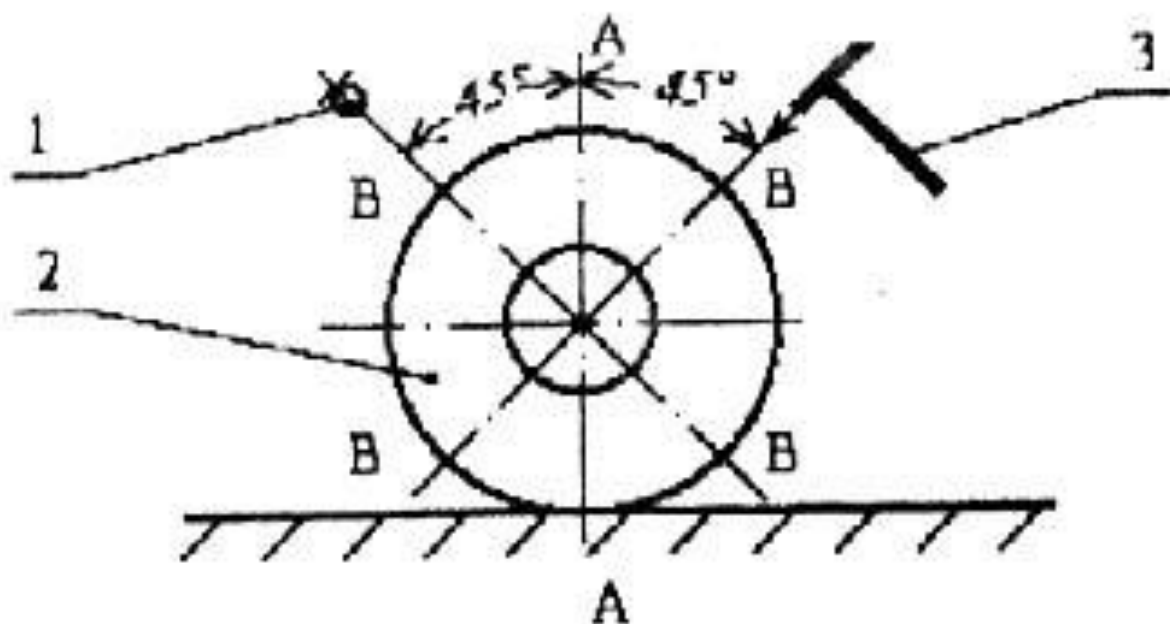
Схема расположения круга при проведении измерений (1 – микрофон; 2 – измеряемый круг; 3 – молоток; AA – диаметр, проходящий через опору; BB – возможные зоны расположения ударника и микрофона)
